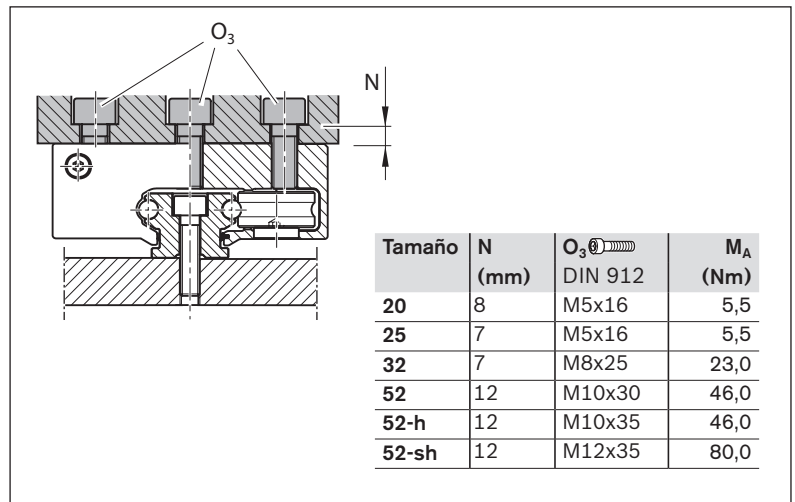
Montar el componente guiado sobre patines de guía estándar y súper
